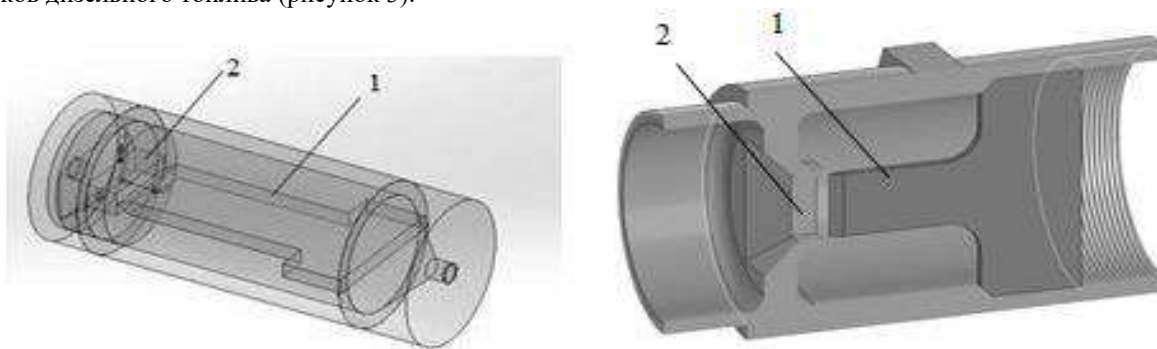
Фото и чертеж конструкции гидродинамического смесителя
